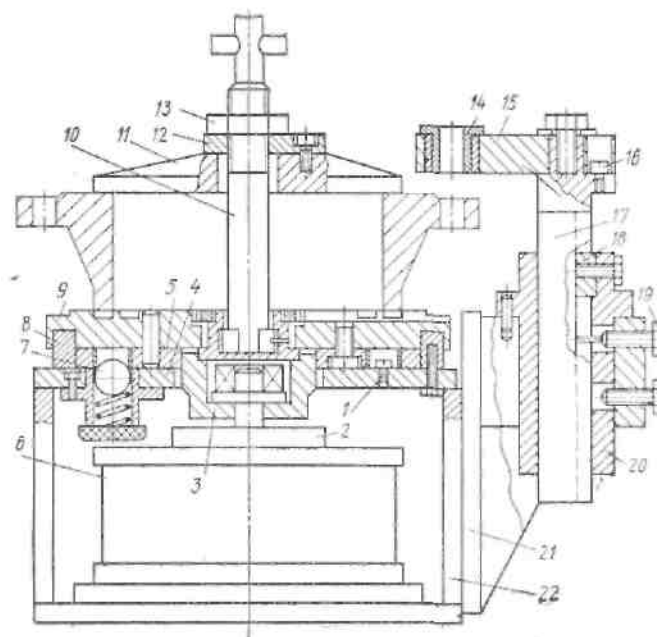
Універсальний поворотний кондуктор із пневматичним затиском для свердління фланців, приварених в стик
